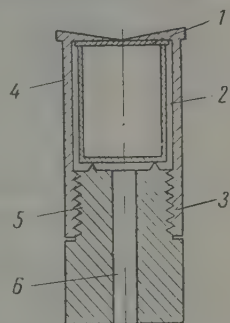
Эффузионная камера: 1 — диафрагма; 2 — вкладыш; 3 — верхний корпус камеры; 4 — верхний конусный торец; 5 — пробка; 6 — отверстие для ввода термопары и подставки
